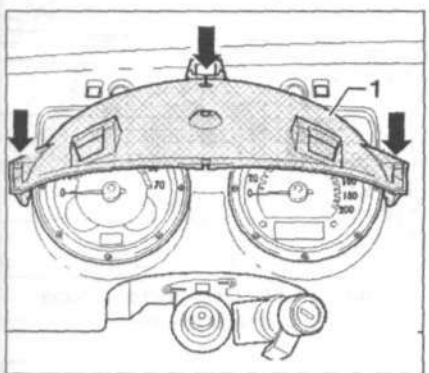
Выкрутите три винта (стрелки) и снимите нижнюю часть козырька 1 щитка приборов.
